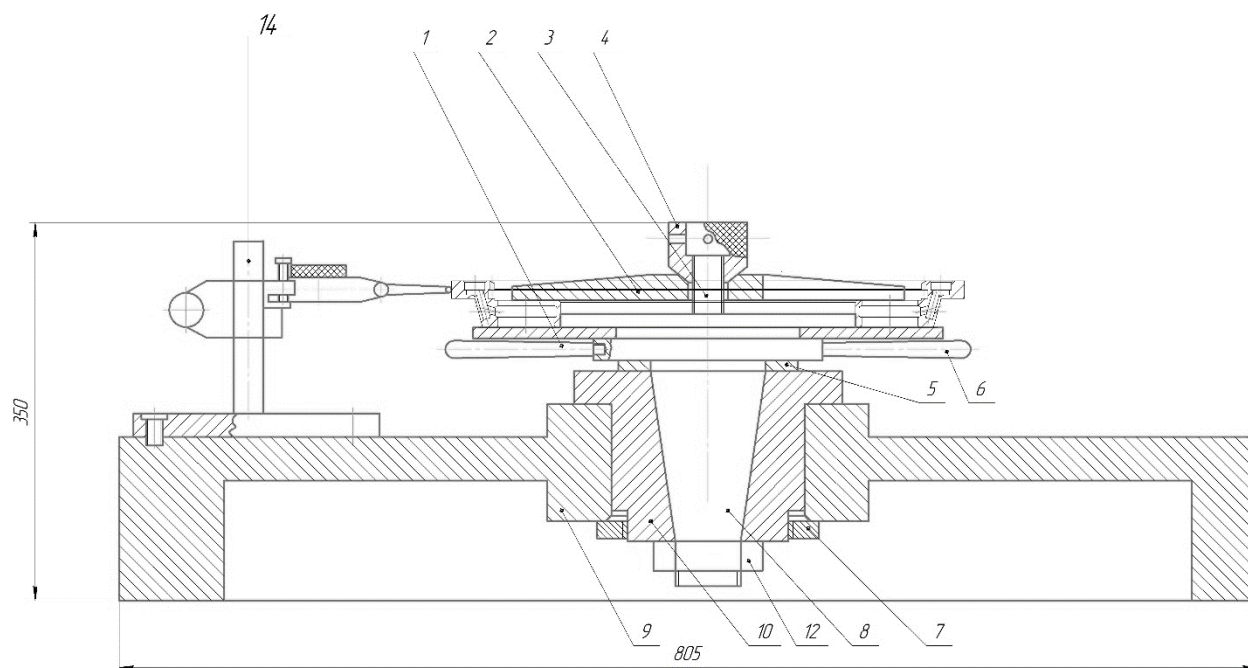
Схема установки деталі в пристосуванні.
